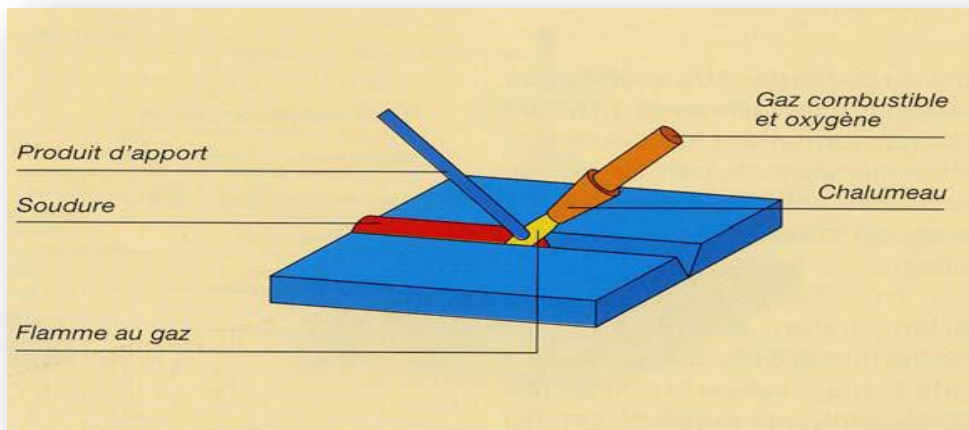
Principe du soudage oxygaz[24]
